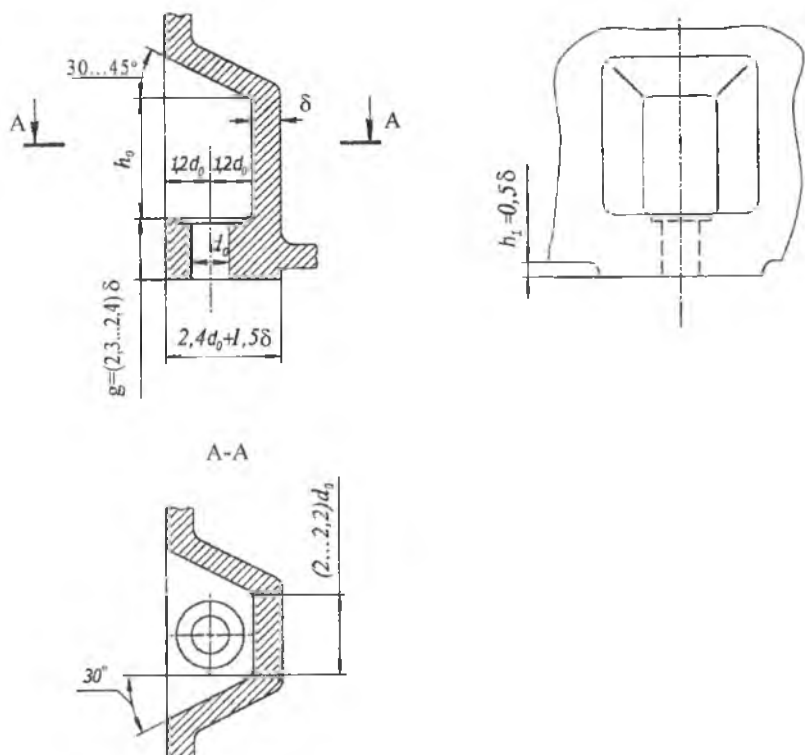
Узел крепления корпуса к основанию на боковой стенке
